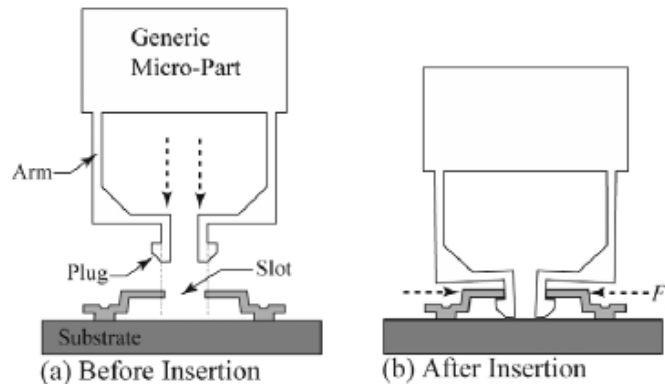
Technique d'assemblage robotisé "Snap Lock Joint" [DeMC04]
